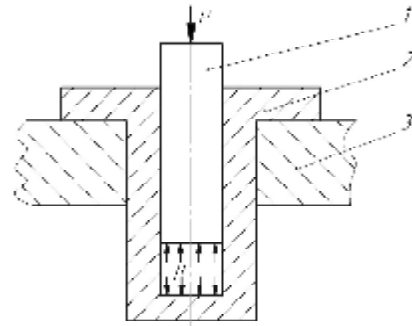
Схема передачі сил: 1 – плунжер; 2 – циліндр; 3 – станина
